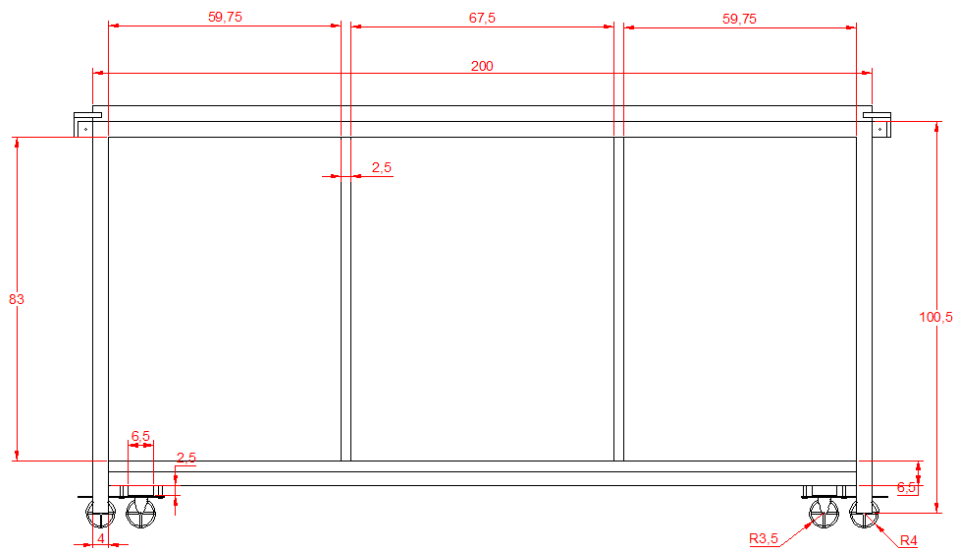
Vista frontal banco de pruebas sin rediseño de las celdas de ensayo
